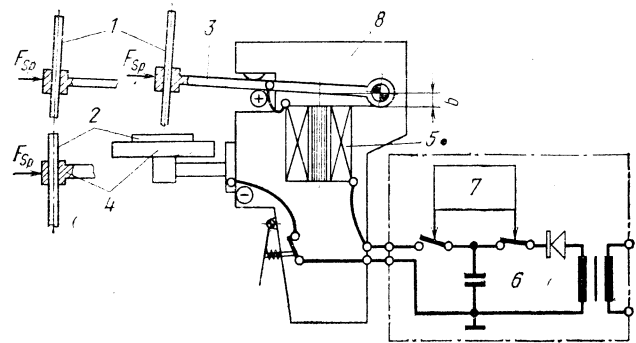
Принцип ударной конденсаторной сварки с магнитным ускорением: 1 — привариваемая проволока; 2 — листовая (проволочная) прокладка; 3 — рычажное ударное устройство с зажимом; 4 — жесткая подкладка с зажимом; 5 — магнитная катушка (катушка-ускоритель); 6 — узел подзарядки конденсатора; 7 — блок управления; 8 — корпус аппарата
